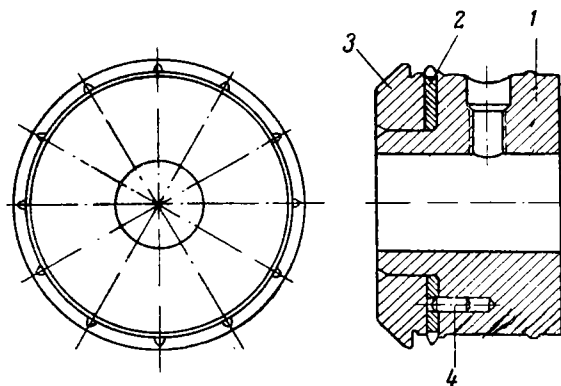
12-зубый барабан кинопроектора ПП-16-1
